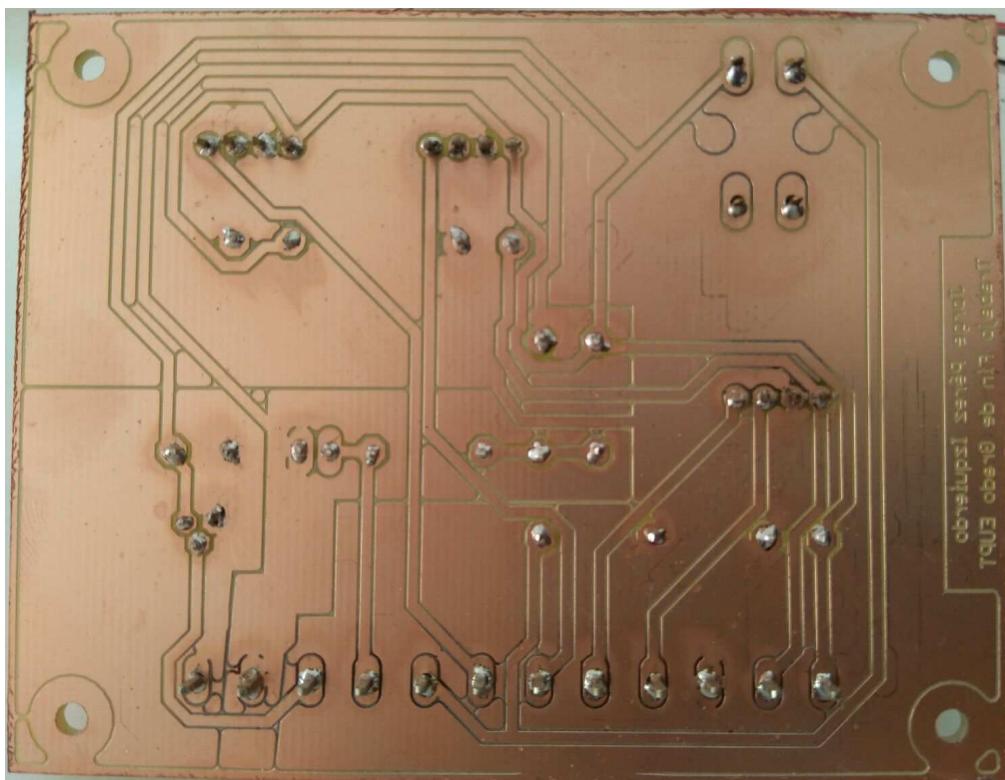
Placa de circuito impreso de los sensores soldada.
